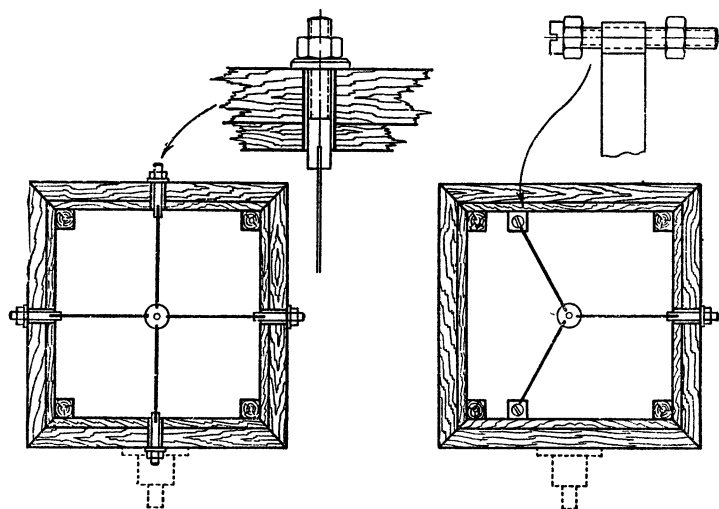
Крестовина из растяжек для укрепления в трубе оправы с диагональным зеркалом (слева — из четырех стальных полосок, справа — из трех). Вверху изображены детали креплений.
